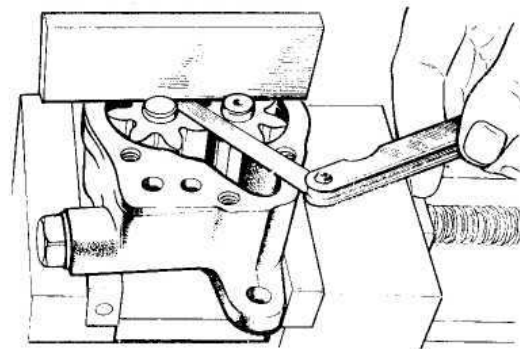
Проверка зазора между торцами шестерён и плоскостью корпуса насоса
